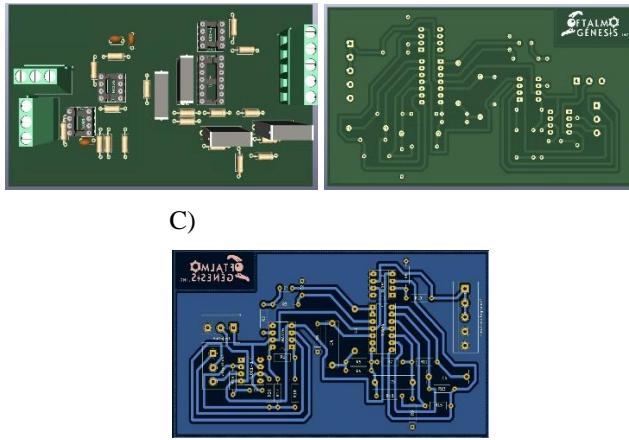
A) Diseño del PCB en el editor de Placas B) Parte superior del PCB donde se pueden observar los componentes electrónicos. C) Parte inferior que muestra las pistas soldaduras.
